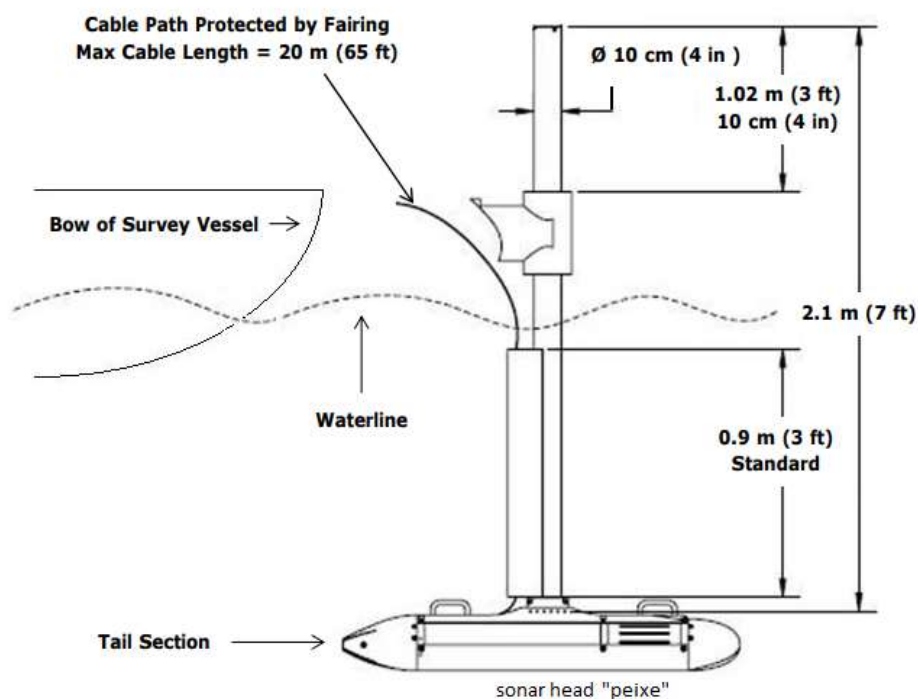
Esquema de montagem do interferômetro segundo instruções do fabricante. Fonte: Manual EdgeTech 4600, adaptado.
